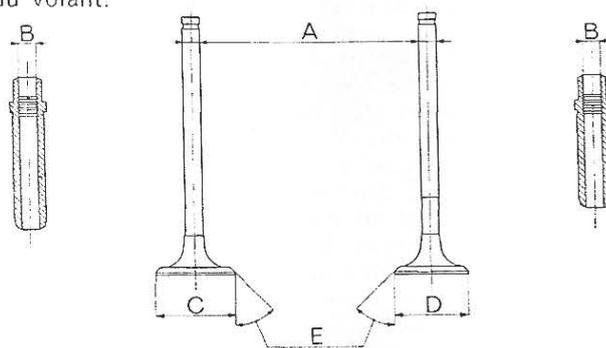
Dimensions principales des soupapes et des guides de soupapes
